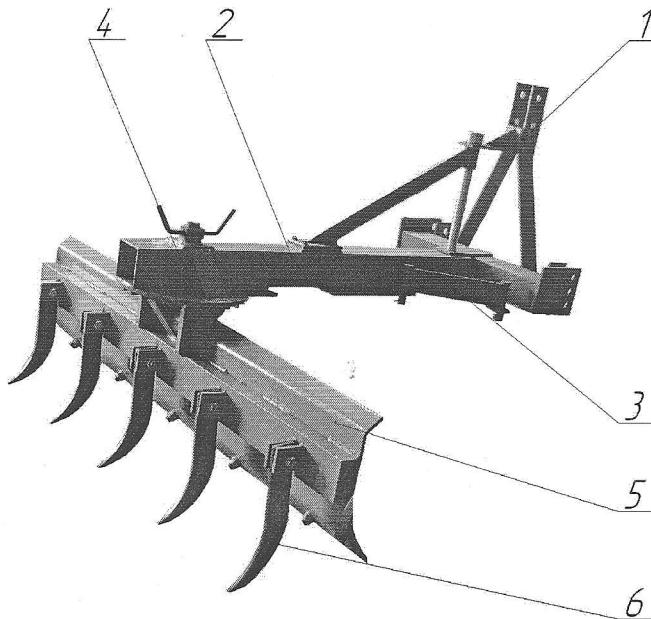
Устройство лопаты рыхлителя-выравнивателя серии GBR
